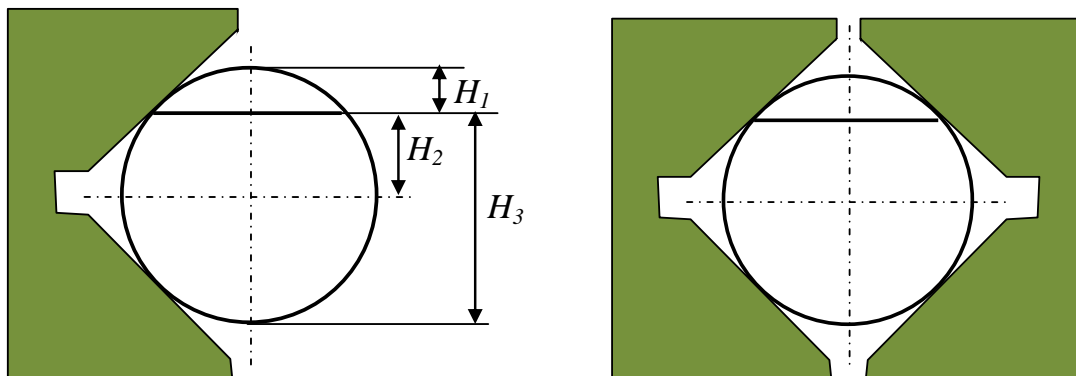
Базування валів на фрезерно-центрувальних верстатах
